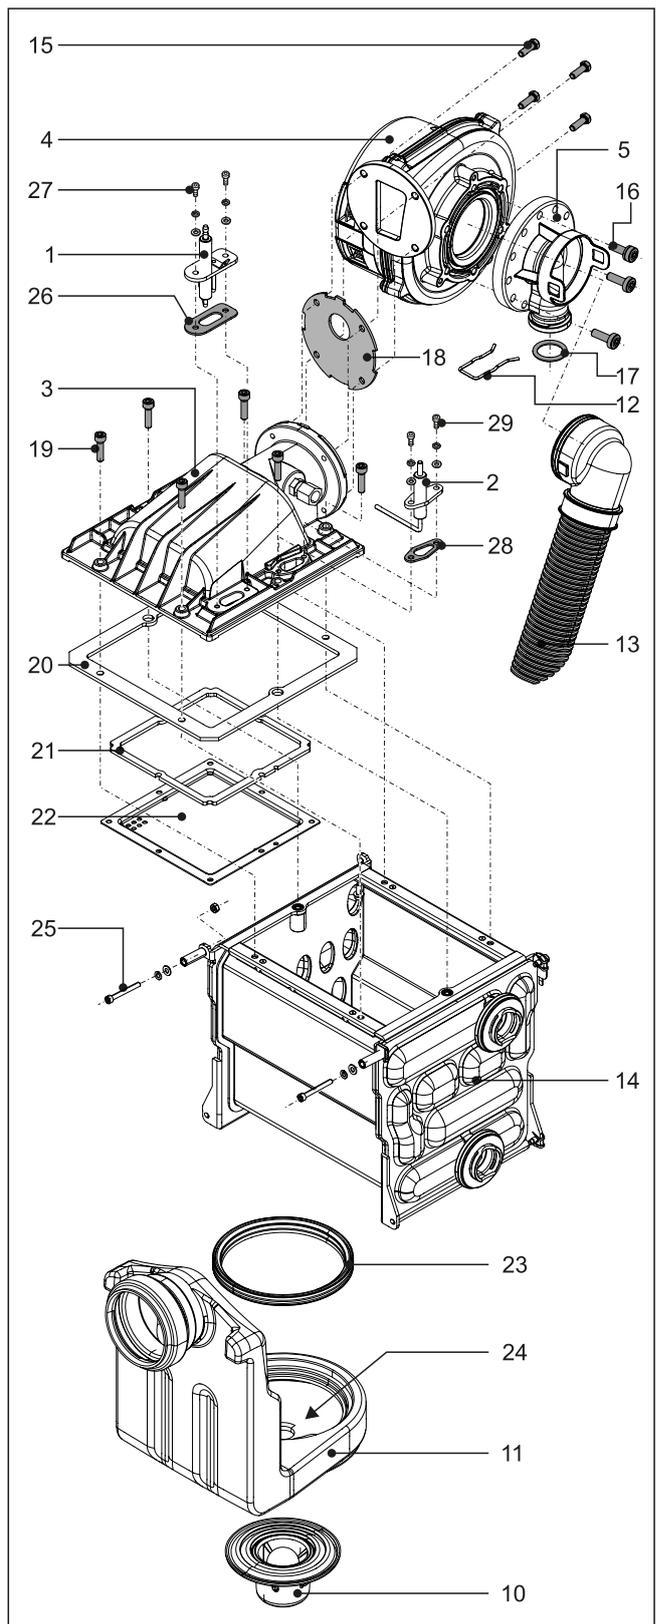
Bauteile der GCU compact – Explosionsdarstellung (Legende siehe Tab. 7-1)
